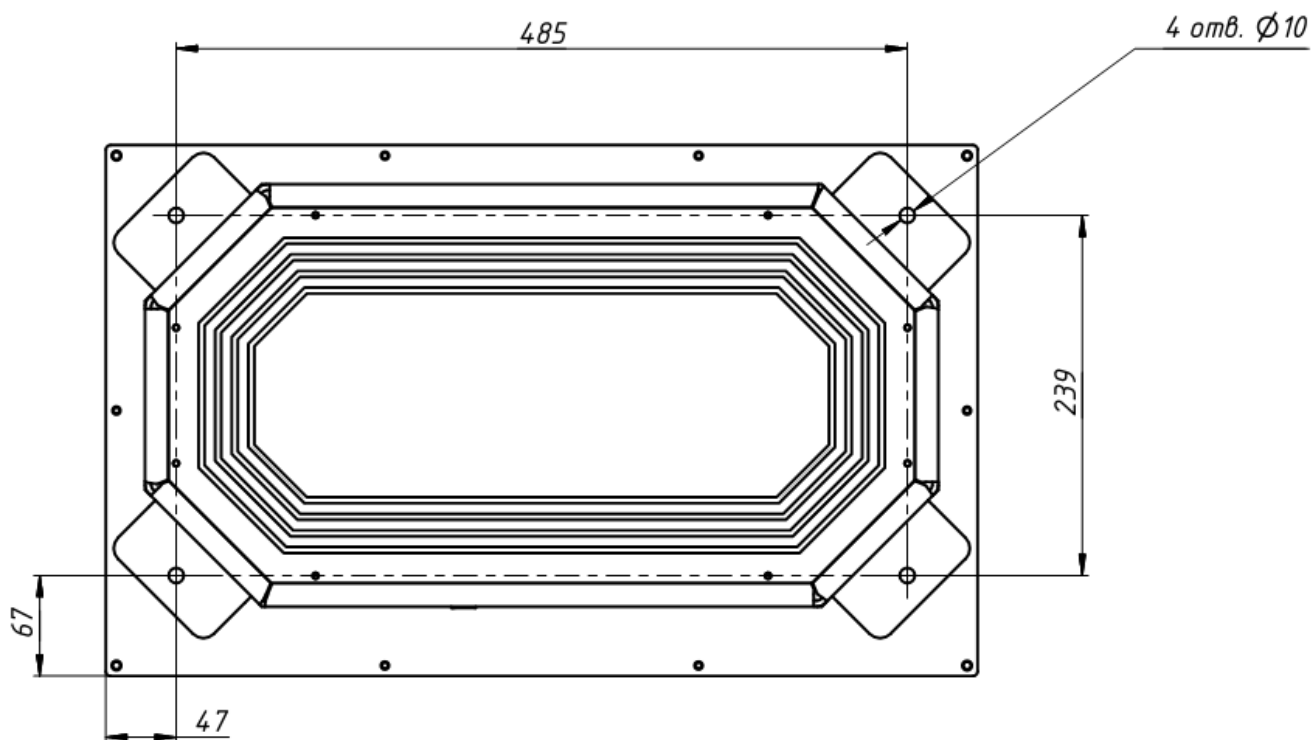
Габаритный чертёж ПИ в исполнении
